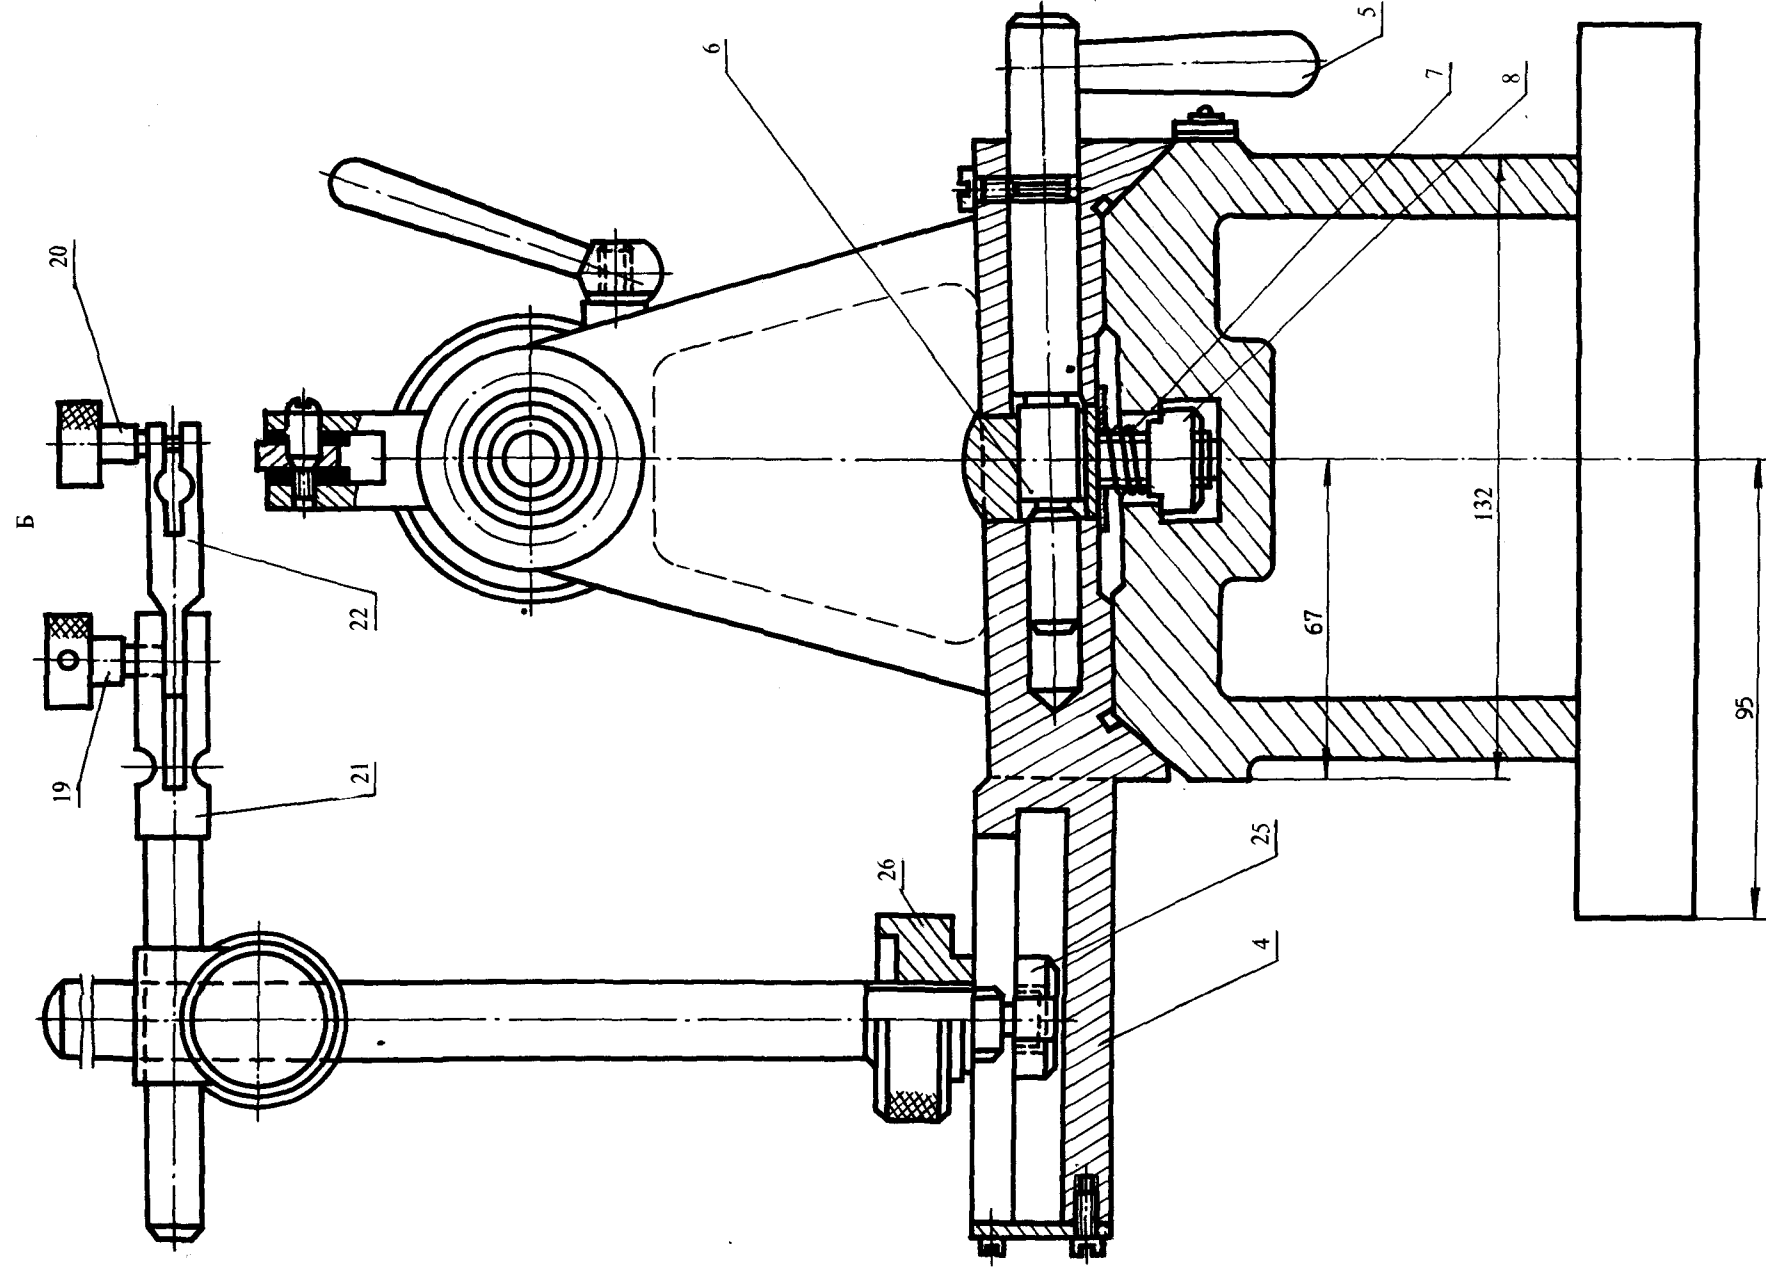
Универсальное приспособление для контроля валов (вид Б на рис. 3.29):
